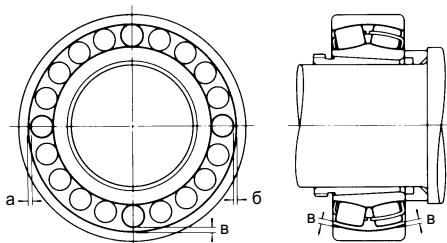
Измерение зазора в большом сферическом подшипнике с бочкообразными роликами
